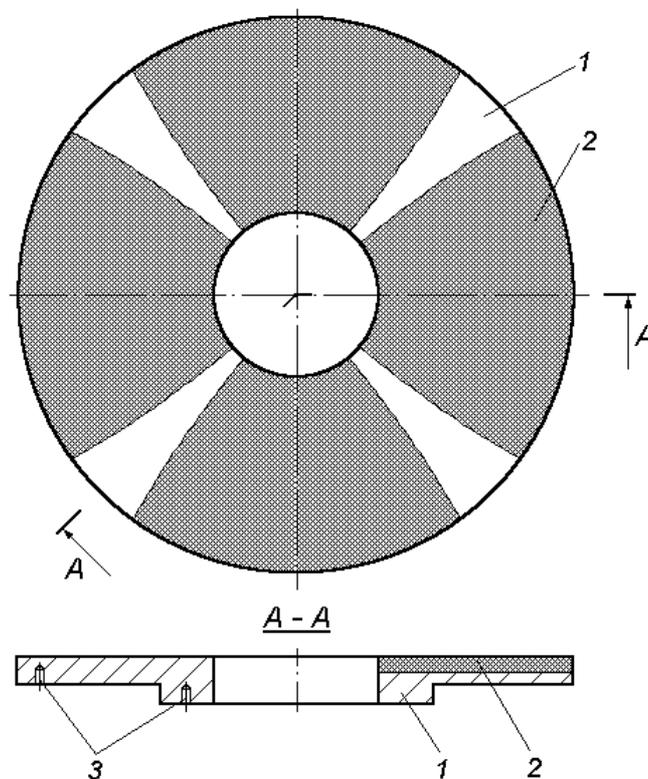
Конструкція металоабразивного плоского притира для чорнового доведення поверхонь
